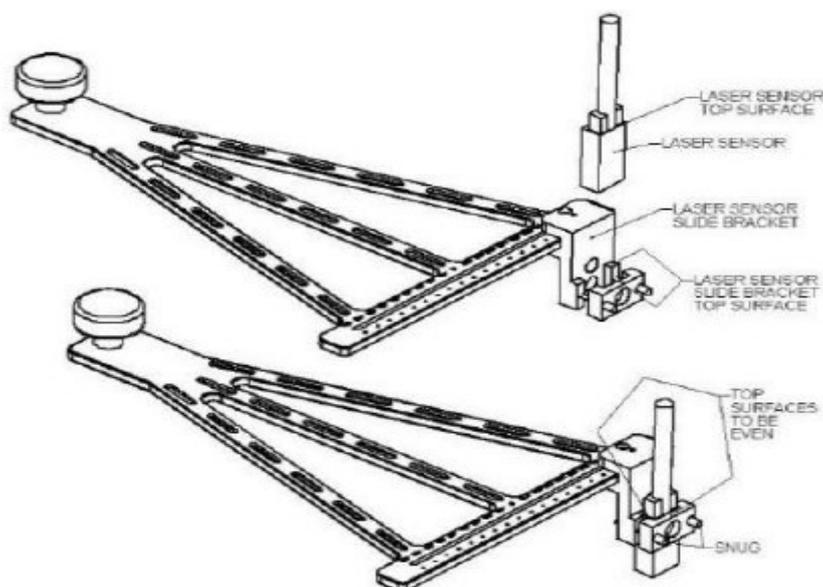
Montagem do sensor de potência do laser no suporte deslizante.
